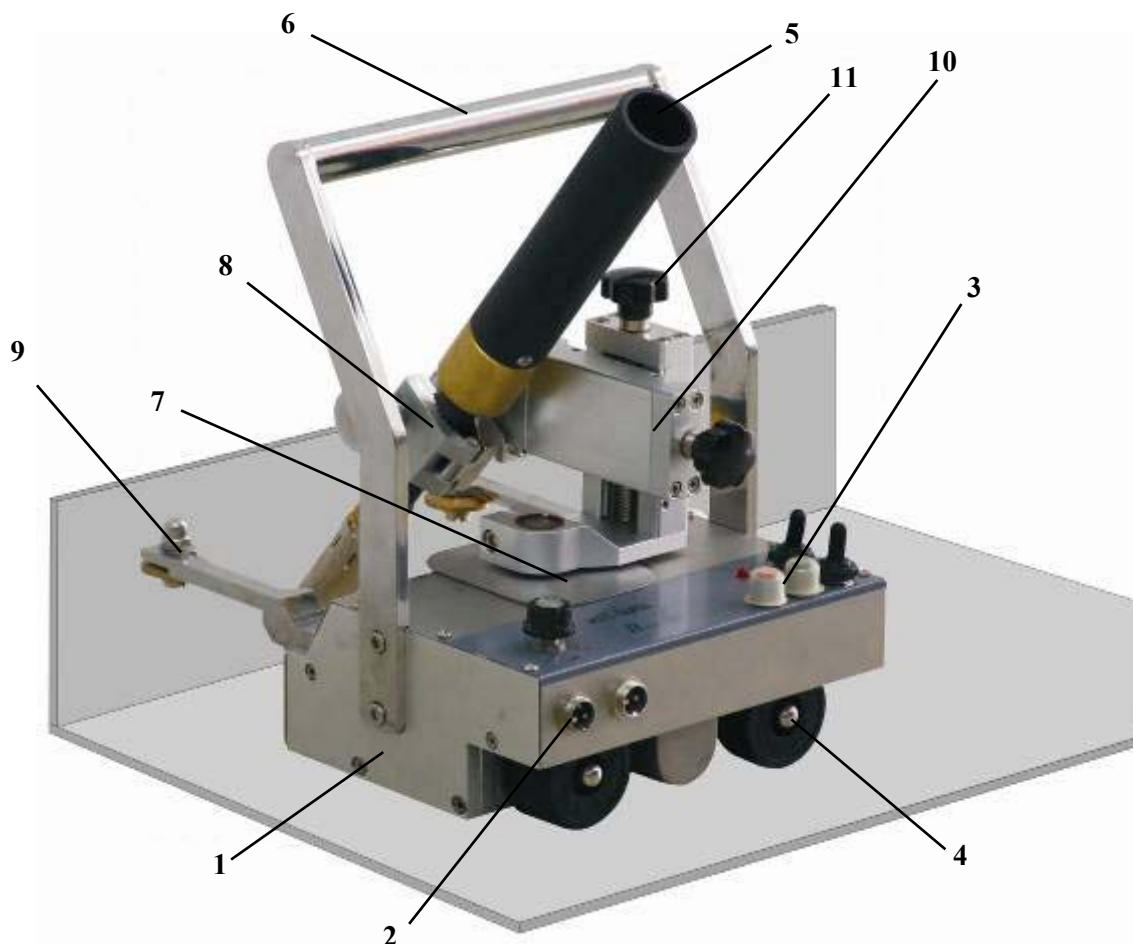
Сварочная каретка HIT-NAW – внешний вид
